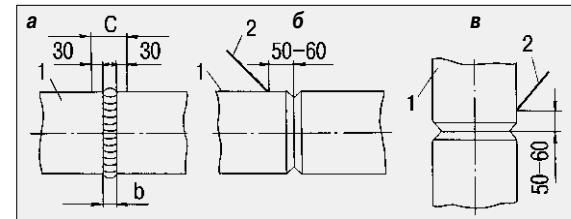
Места крепления горячего спая термоэлектрического преобразователя при термообработке и подогреве для сварки:
